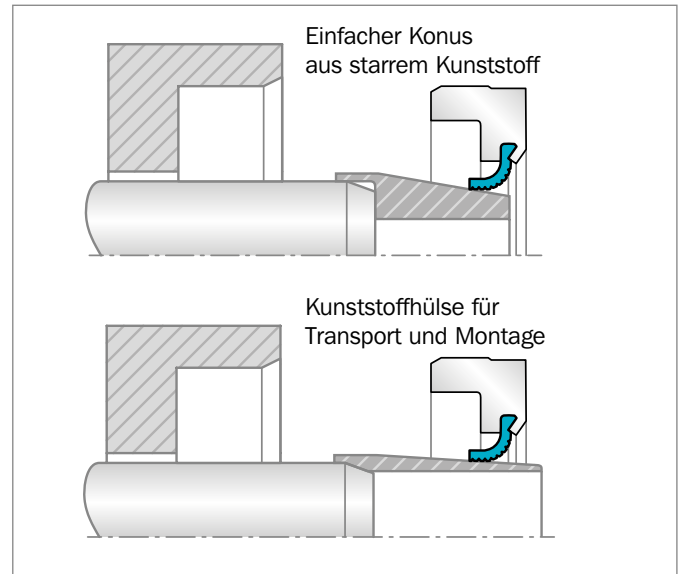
Montagewerkzeuge für den Einbau auf Wellen
